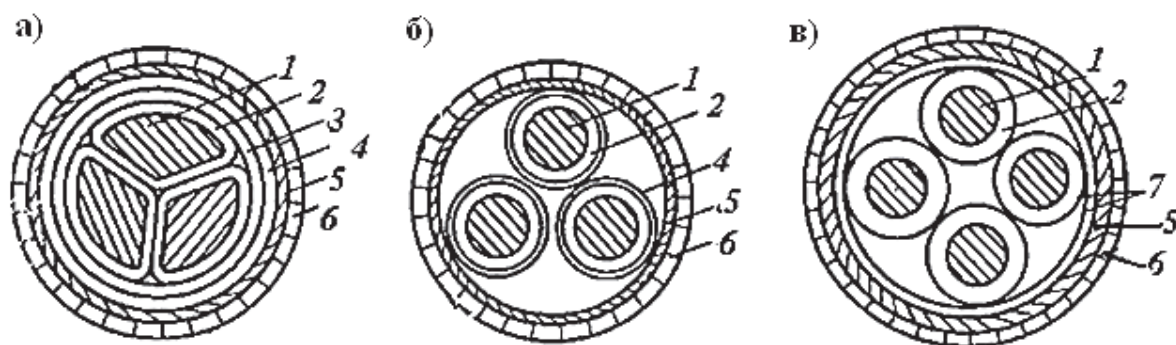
Конструкция кабелей 1...35 кВ: а – кабель на напряжение до 10 кВ с бумажной изоляцией; б – то же с резиновой изоляцией; в – то же на напряжение 20 и 35 кВ; 1 – токопроводящая жила; 2 – фазная изоляция; 3 – поясная изоляция; 4 – свинцовая или алюминиевая оболочка; 5 – броня; 6 – защитные покровы; 7 – обмотка лентой
